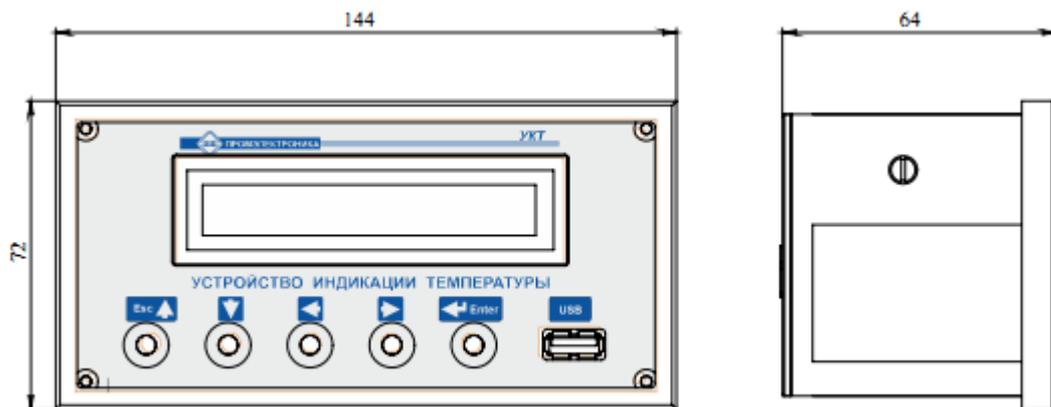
Габаритные и присоединительные размеры УИТ
